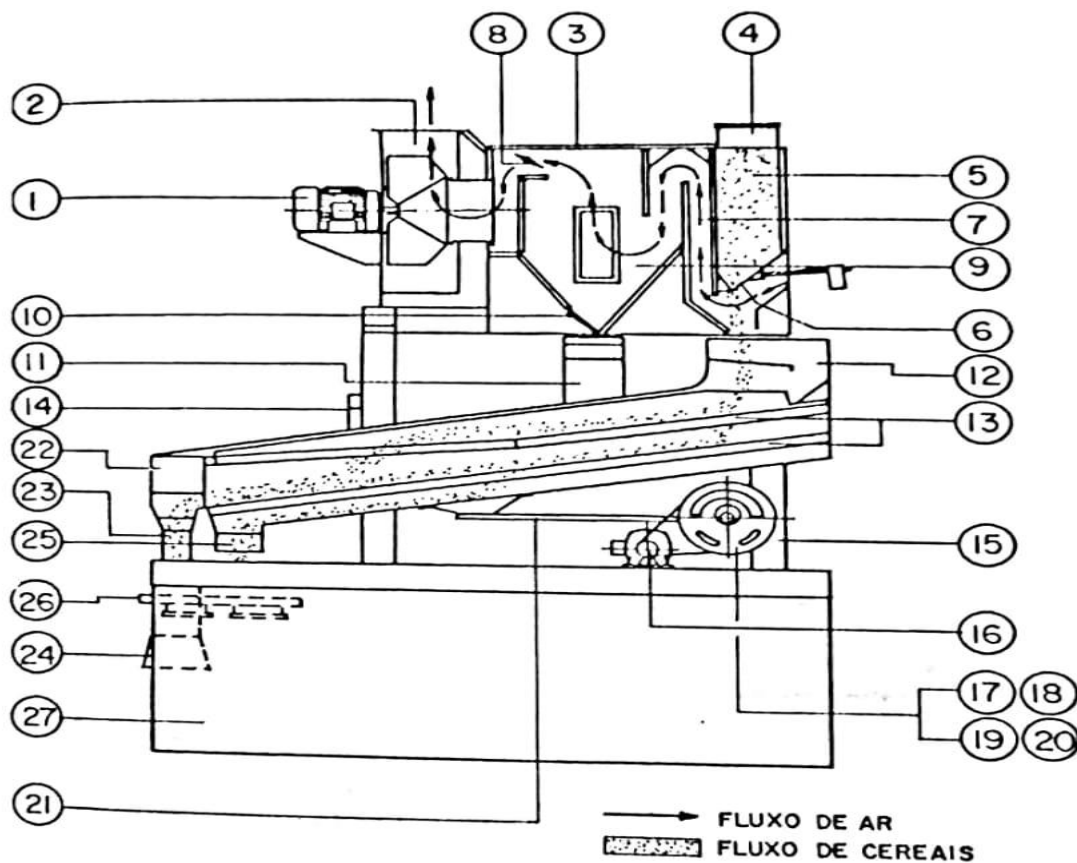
Máquina de Pré-Limpeza: corte longitudinal.
